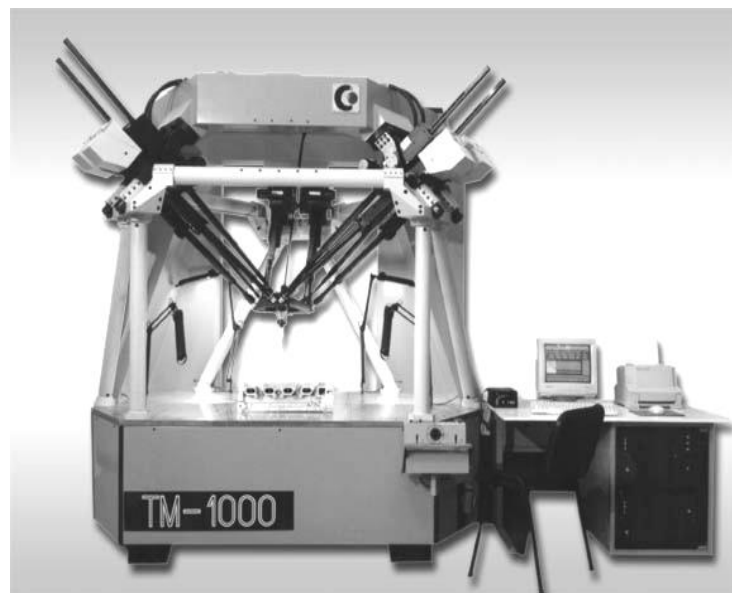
Загальний вигляд обробного центра мод. ТМ-1000АО "Лапик"
